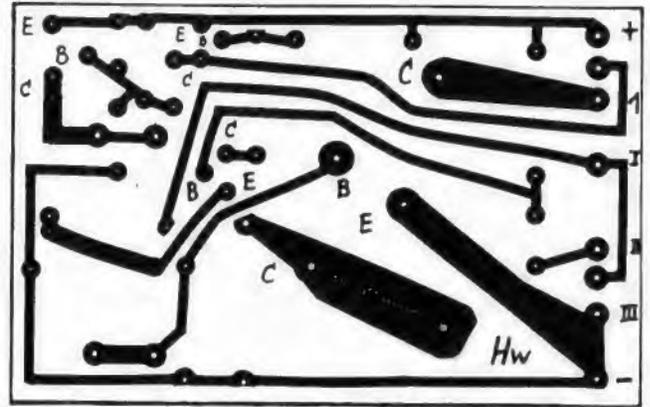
Platine mit Bestückung (Maßstab 1 : 1)
